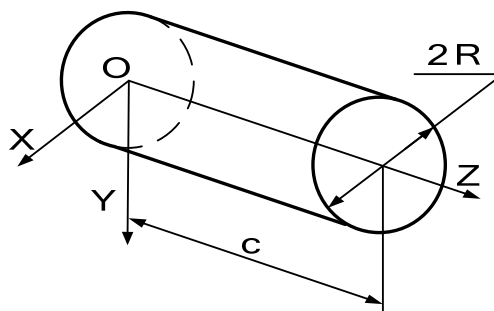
Цилиндрическая и торцевая поверхность, обрабатываемая на станке
